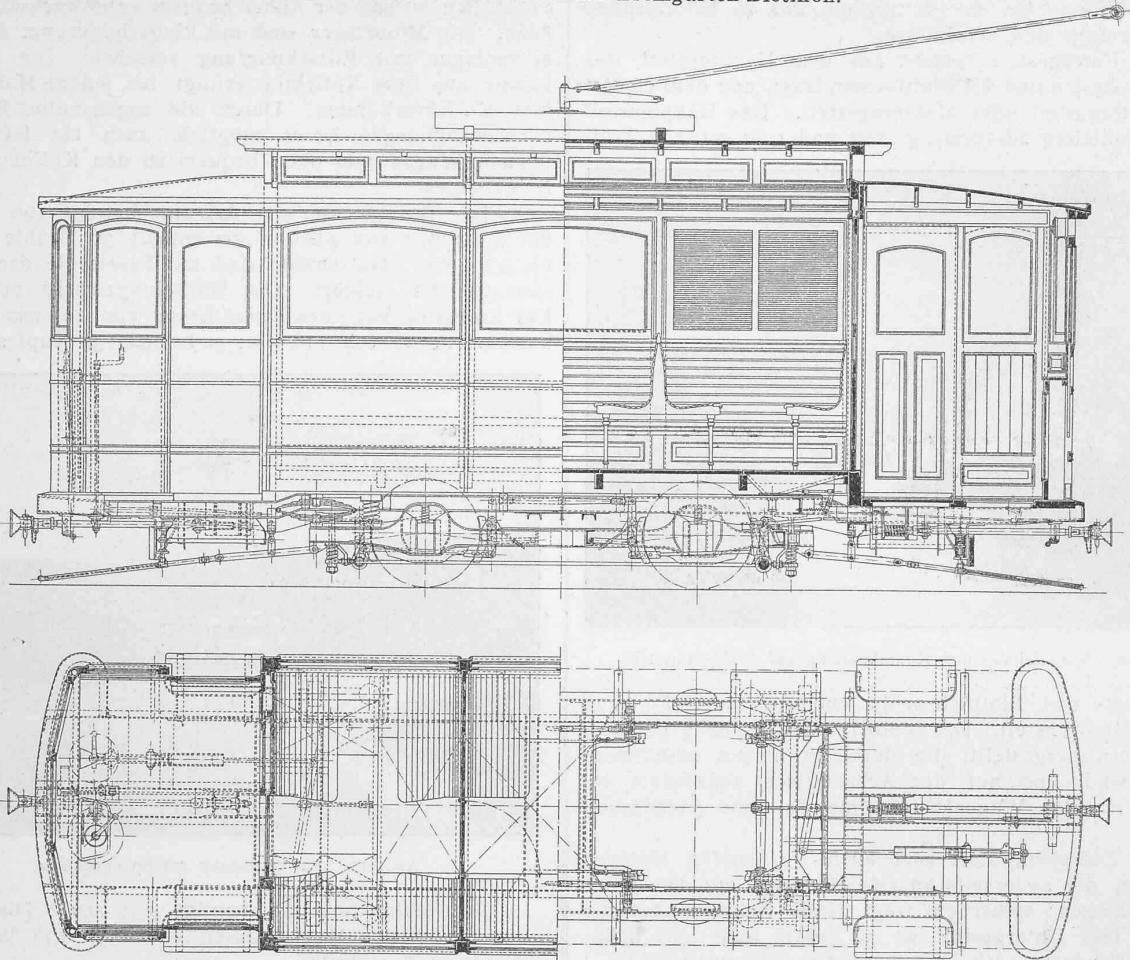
Motorwagen. — Ansicht, Grundriss und Schnitt. — Masstab 1:50.
